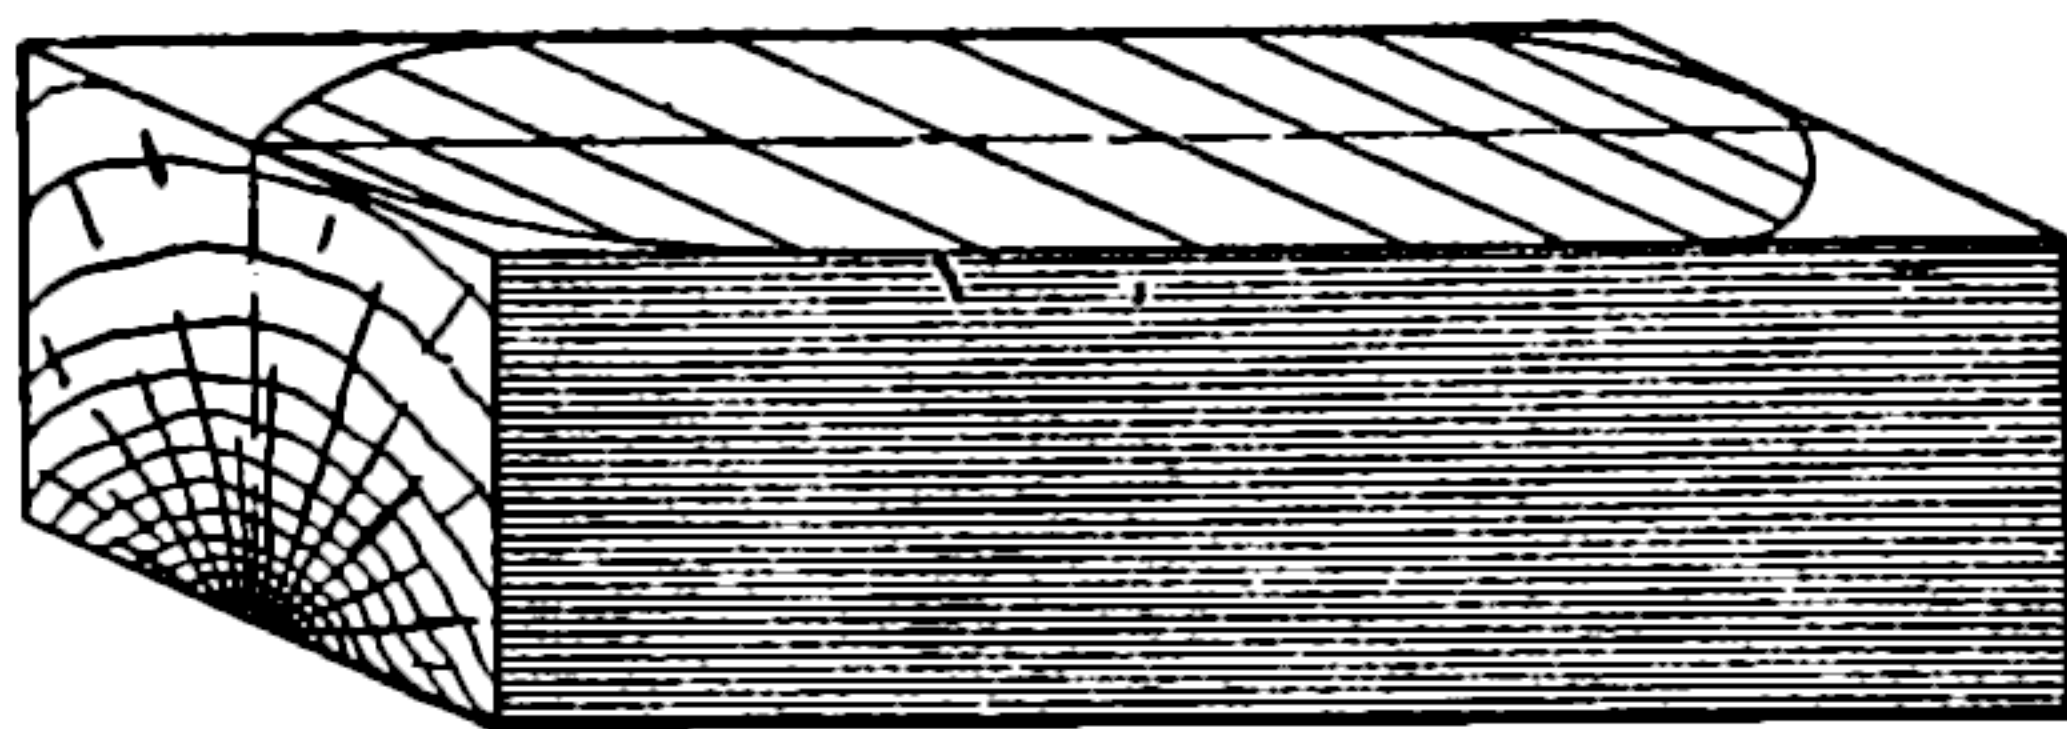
Деревянная болванка, из которой надо сделать корпус судна. Сверху болванки обведен контур палубы.
